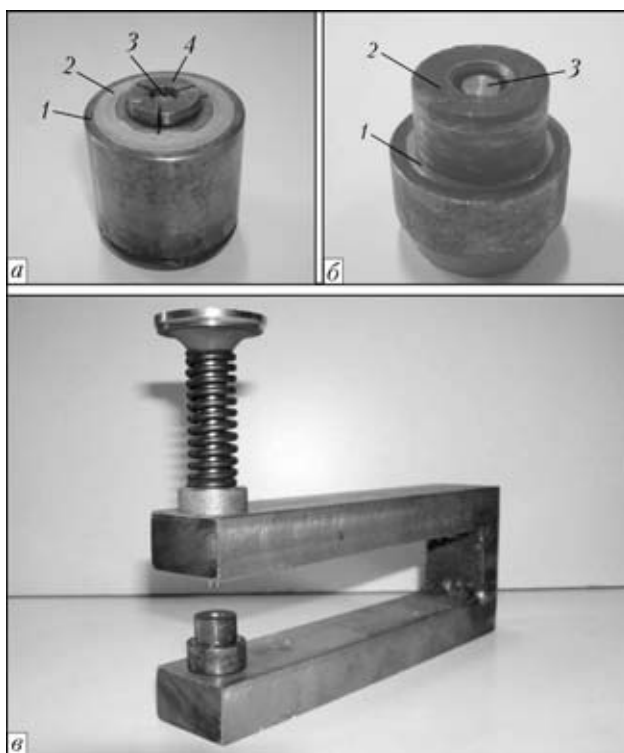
Устройства для формирования соединений методом продавливания: а — раскрывающаяся Clinch-матрица (1 — формующая головка цангового типа; 2 — наковальня; 3 — эластичная муфта; 4 — кондуктор); б — сборно-разборная ТОХ-матрица (1 — формующая втулка; 2 — регулировочная прокладка; 3 — наковальня); в — внешний вид скобы
